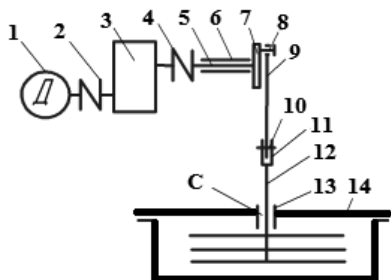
Схема електромеханічного кривошипно-шатунного привода
